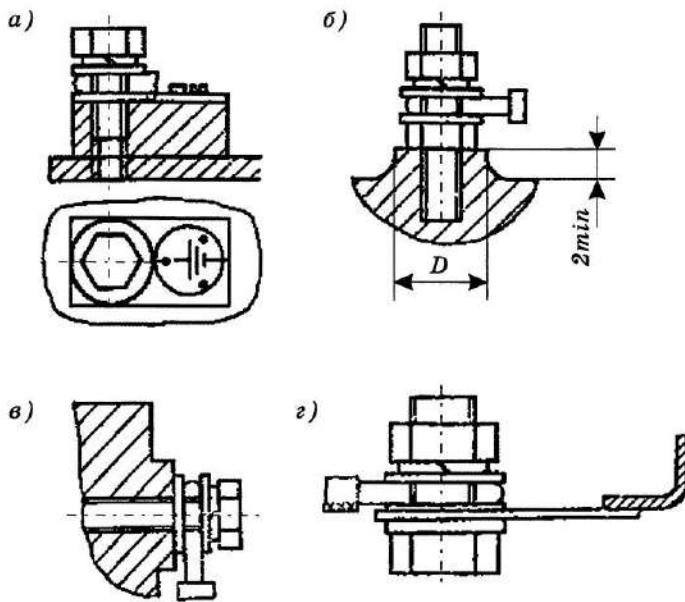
Варианты установки зажимов: а — на прямоугольное изделие; б — на прилив; в — на прилив, установленном сбоку изделия; г — на листовом корпусе
